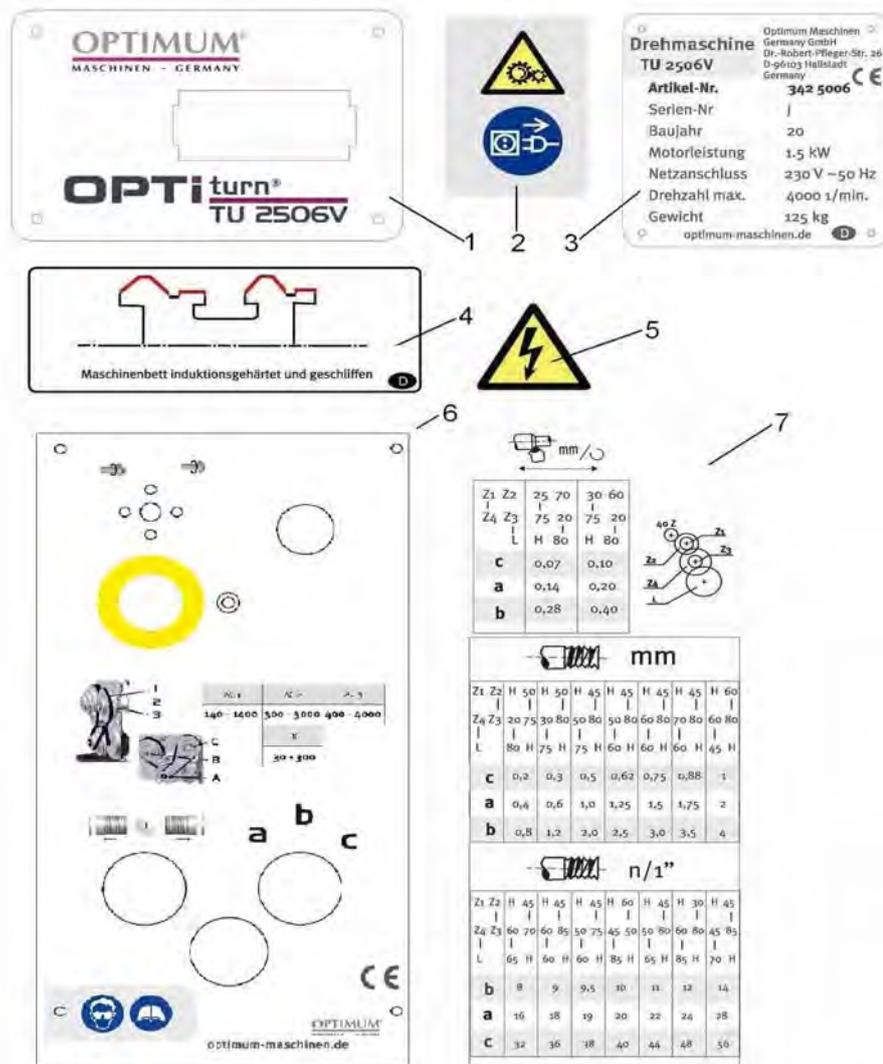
Maschinenschilder - Etiquetas de máquina
